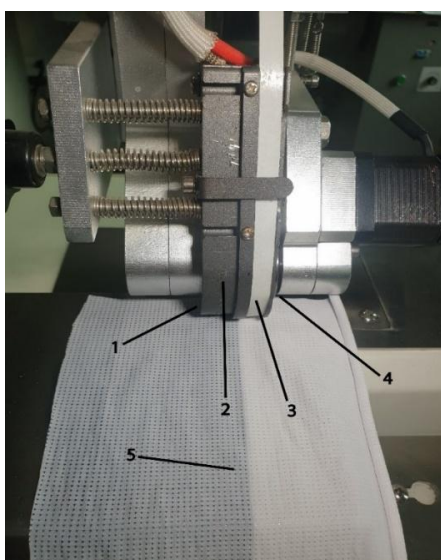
Технологический процесс формирования бесшовного клеевого соединения с использованием KV1300 – 600С: 1 – транспортирующий ролик, 2 – нагревательный элемент, 3 – двусторонняя термоклеевая лента, 4 – ультразвуковой нож, 5 – заготовка обрабатываемой детали
